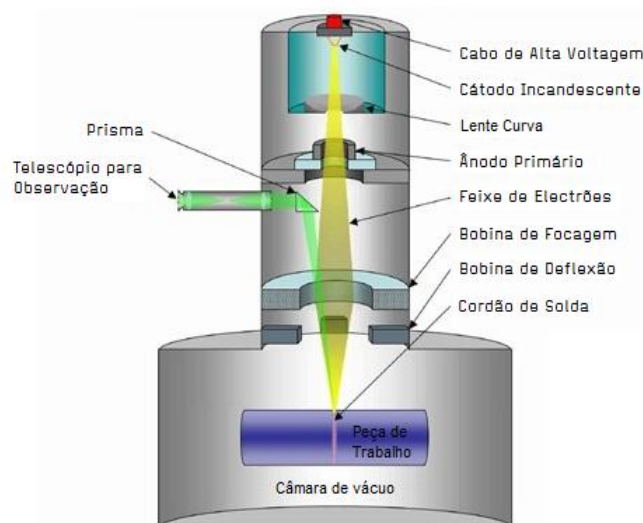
Processo de fusão por feixe de eletrões, EBM [adaptada de <http://www.joiningtech.com/industry-references/welding-types/electron-beam-welding>]
